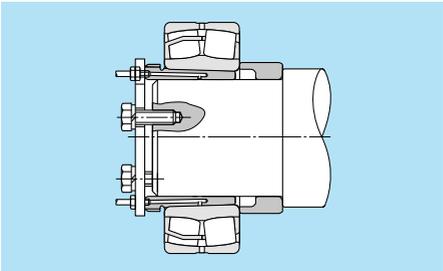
Montage mit hydraulischer Abziehhülse
